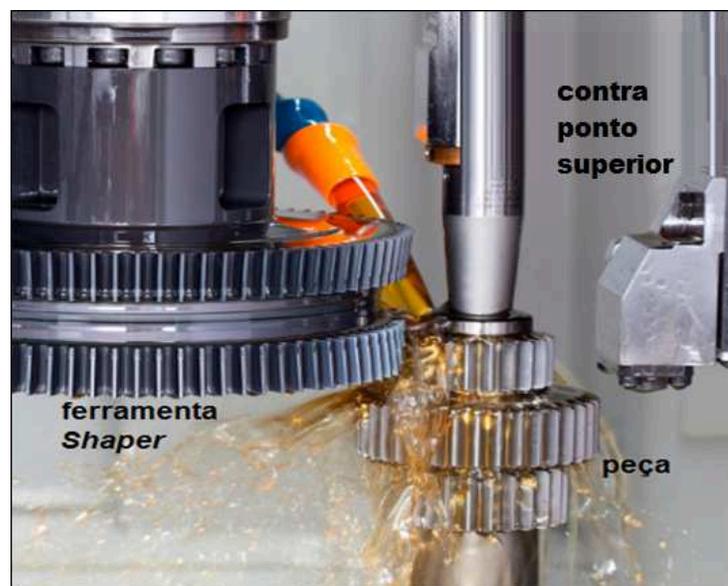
Engrenagens fabricadas pelo Processo *Shaper
